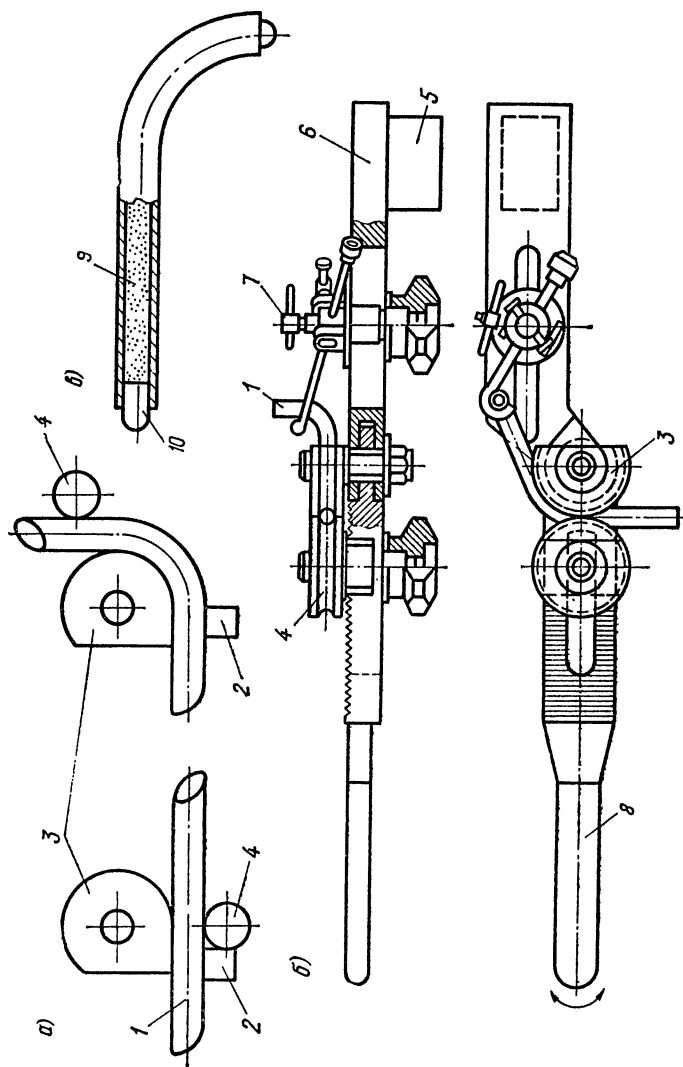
Гибка труб: а — схема гибки; б — приспособление для гибки вручную; в — гибка труб с наполнителем
